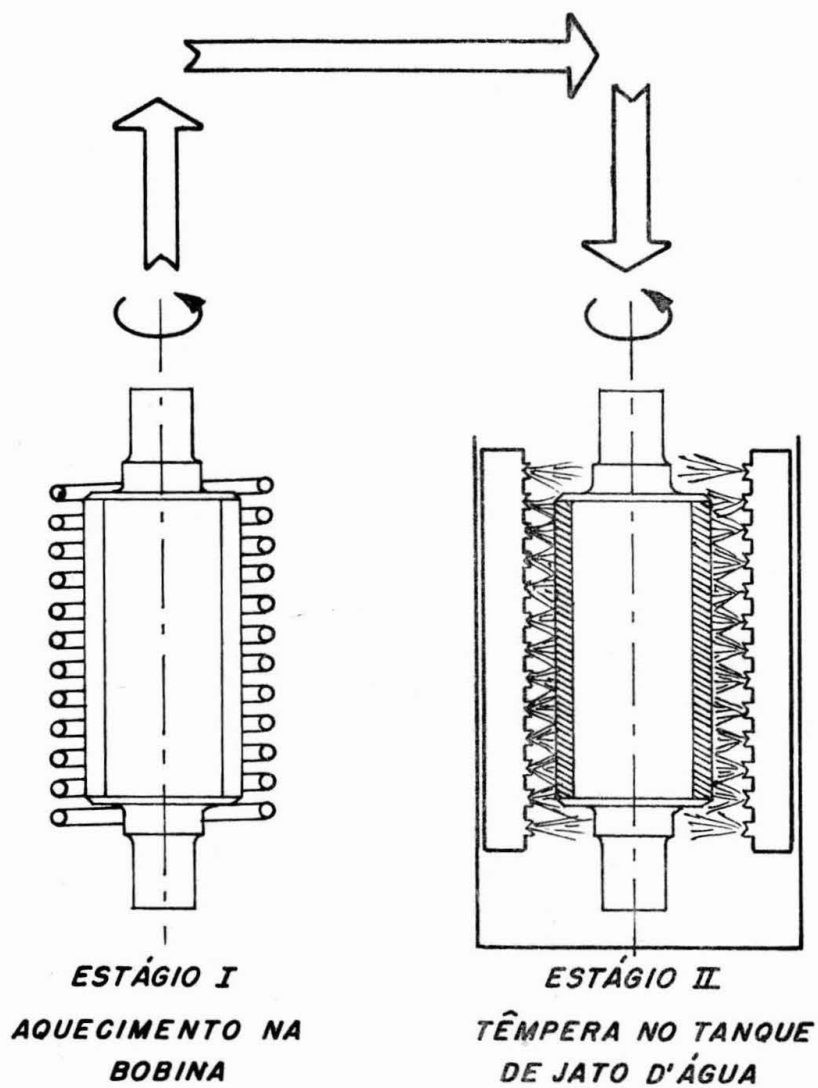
SISTEMA DE ENDURECIMENTO DE
